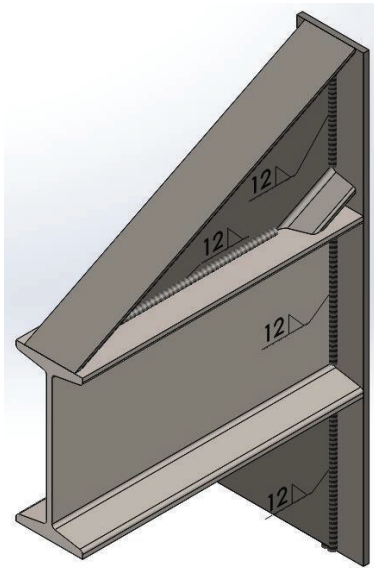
Soldadura configuración perfil ipn.
